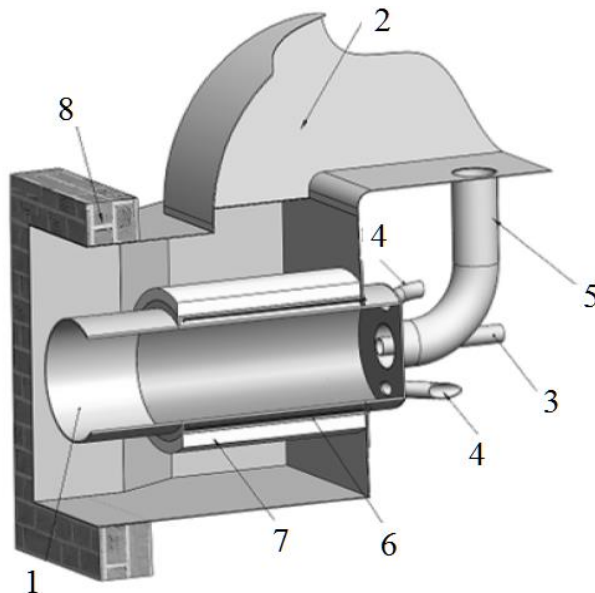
Эскиз универсального энергоэффективного горелочного устройства: 1 — реакционная труба; 2 — короб подвода вторичного воздуха; 3 — устройство подвода пыли высокой концентрации (ПВК); 4 — тангенциальный патрубок подачи первичного воздуха; 5 — патрубок осевой подачи первичного воздуха; 6 — система нагрева; 7 — тепловая изоляция; 8 — амбразура котла.
